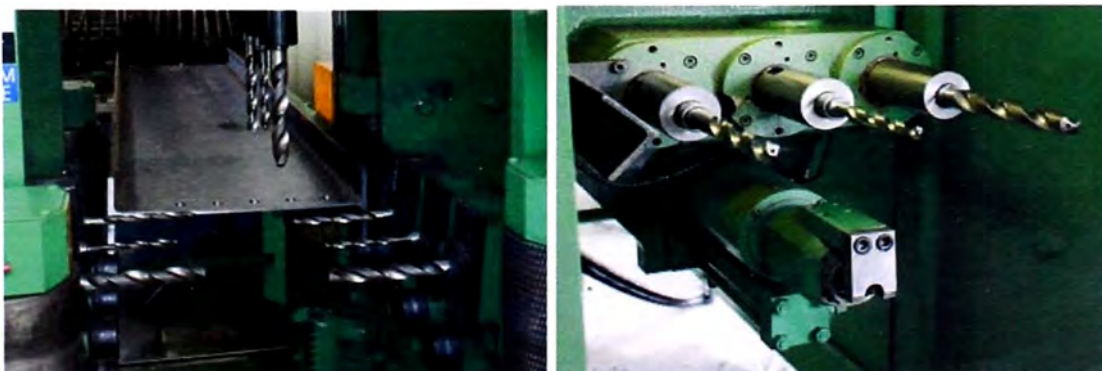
Máquina CNC-BDL (Perforadora y Cortadora de Vigas y Canales)
